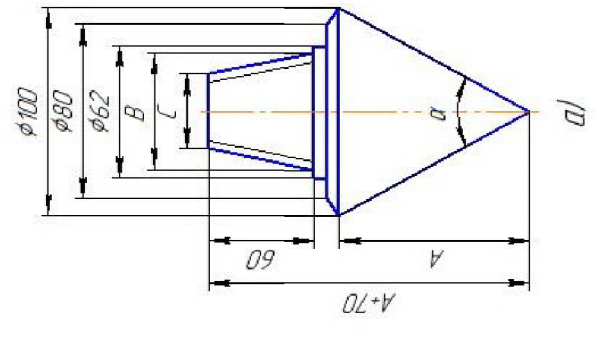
Інструмент для ударно-вібраційного зондування
